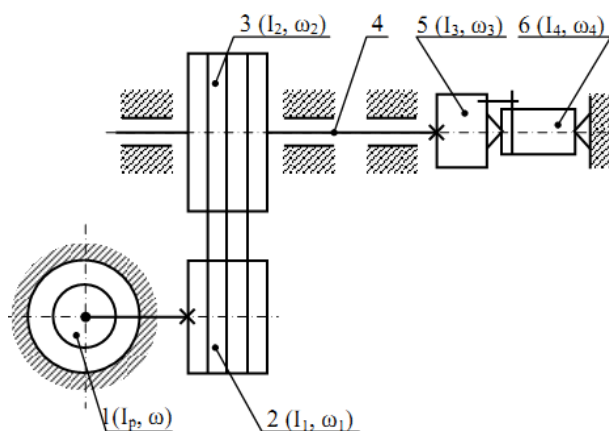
Схема приводу обертання заготовки верстата 3М152
